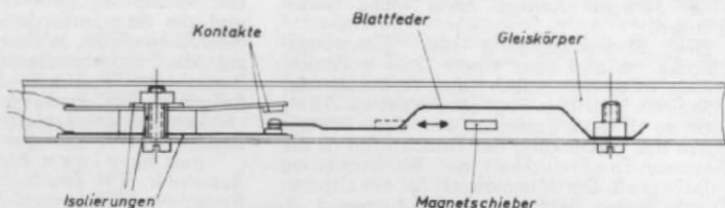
Seitenansicht des Rückmeldeschalters. Die Kontakte und die Blattfeder werden mit je einer M 2-Schraube am Gleiskörper befestigt. Das „Kontaktpaket“ darf nicht über den Gleiskörper herausragen; ggf. müssen die beiden Kontakte, wie angedeutet, etwas auseinandergebaugen werden.
